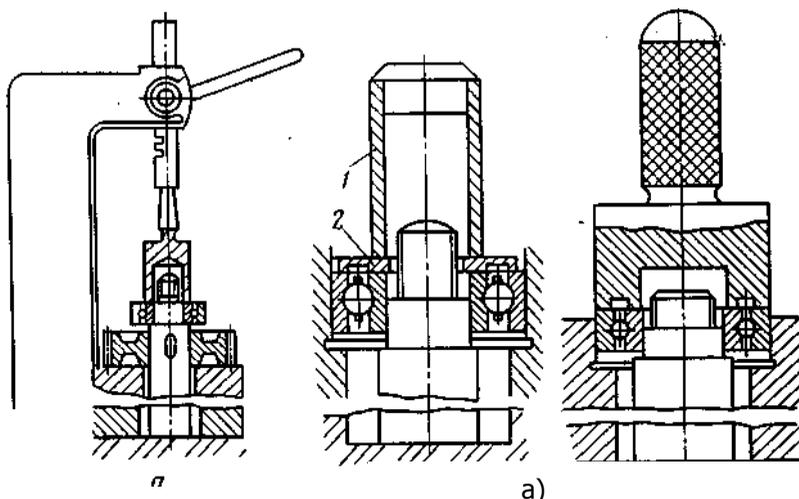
Приспособление для напрессовки подшипников:
